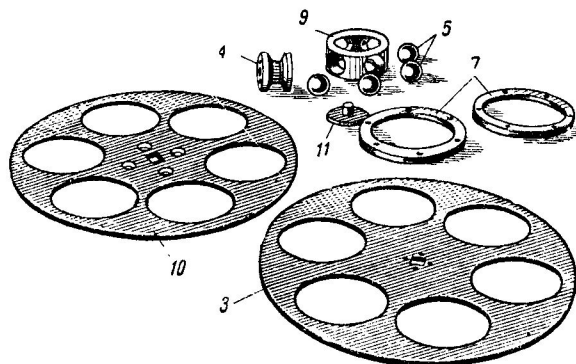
Детали приставки: 3 — ведущий диск; 4 — конус; 5 — шарики; 7 — кольца конуса: подвижное и неподвижное; 9 — сепаратор; 10 — ведомый диск; 11 — центрирующий штифт
